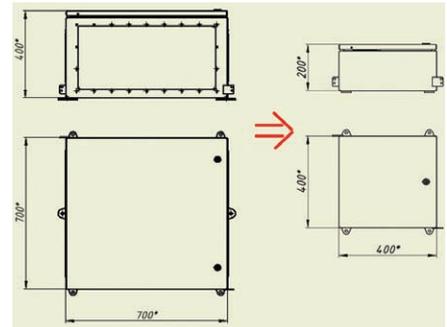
Обновление чертежных видов корпуса навесного КН-2
